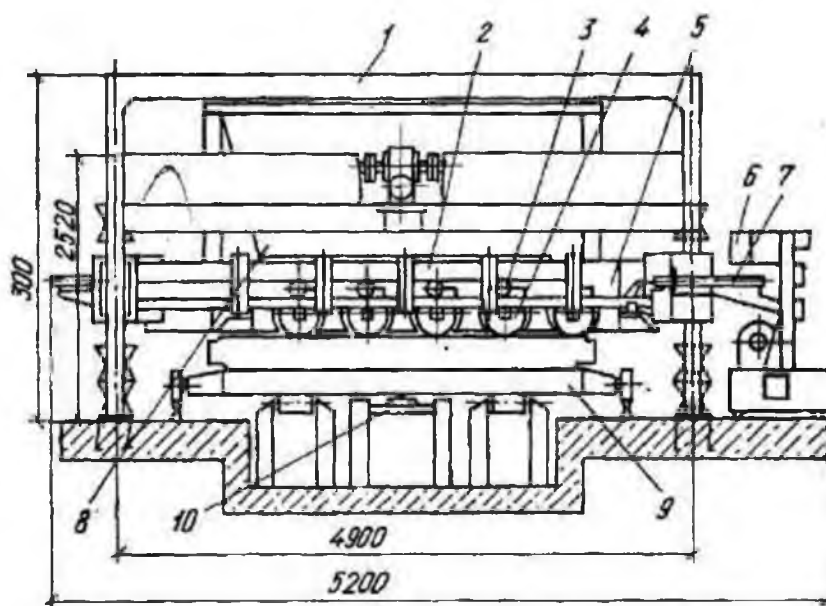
Конструкція безвібраційної роликової формувальної установки
